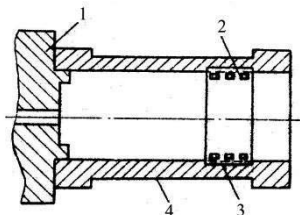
Схема індукційного відцентрового наплавлення гільз циліндрів: 1 – кулачки обертача; індуктор; 3 – шихта; 4 – відновлювана гільза
